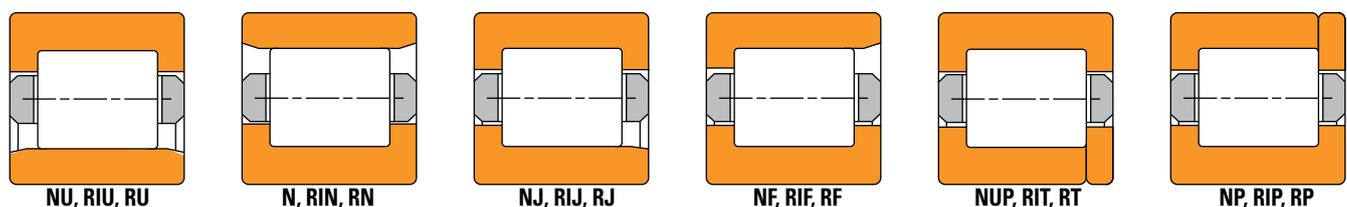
Rodamientos de rodillos cilíndricos radiales.
